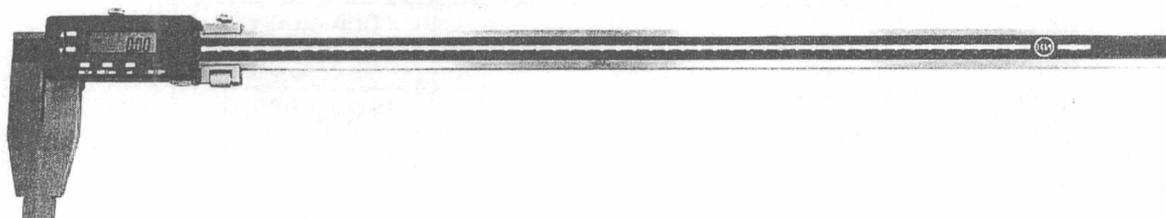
Общий вид штангенциркулей типа ШЦЦ-III
